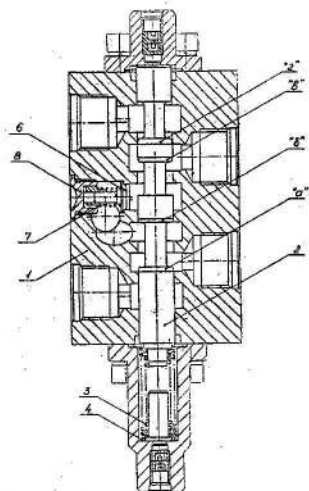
Устройство приоритетного клапана: 1 — корпус; 2 — золотник; 3, 4 — пружины; 5, 6, 7, 8 — детали обратного клапана.
